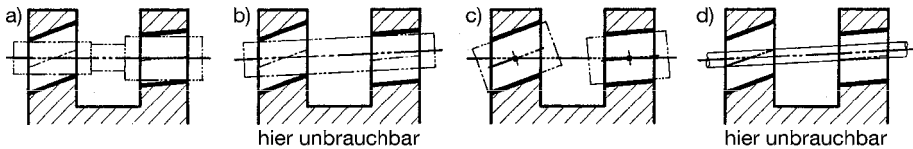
Ableitung einer gemeinsamen Bezugsachse aus zwei Bohrungen. a) Achse von zwei coaxialen Pferchzylindern; b) gemeinsamer Pferchzylinder (nicht funktionsgerecht), c) Verbindung der Mitten zweier Pferchzylinder, d) kleinster Hüllzylinder um die Achsen der Pferchzylinder nach c oder auch um die Istachsen (beides nicht funktionsgerecht)
